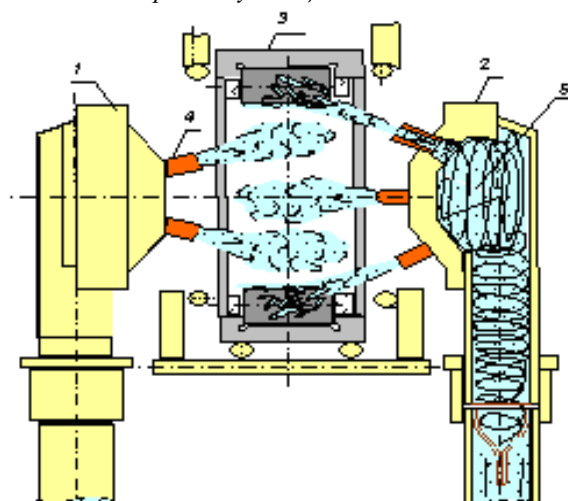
Установка для промывки буксовых подшипников: 1, 2 – струйно - кавитационные головки; 3 – промываемый подшипник; 4 – сопла; 5 – кавитатор
